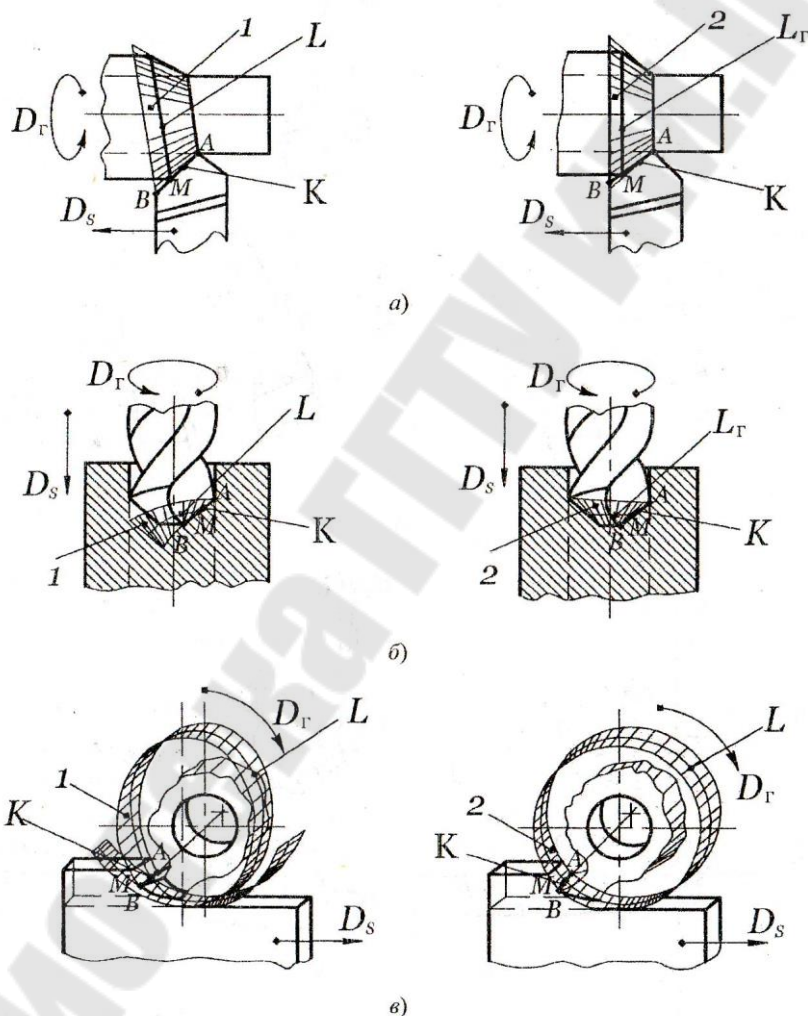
Поверхность резания и поверхность главного движения при продольном обтачивании (а), сверлении (б) и периферийном фрезеровании (в): 1 – поверхность резания R ; 2 – поверхность главного движения R_r
